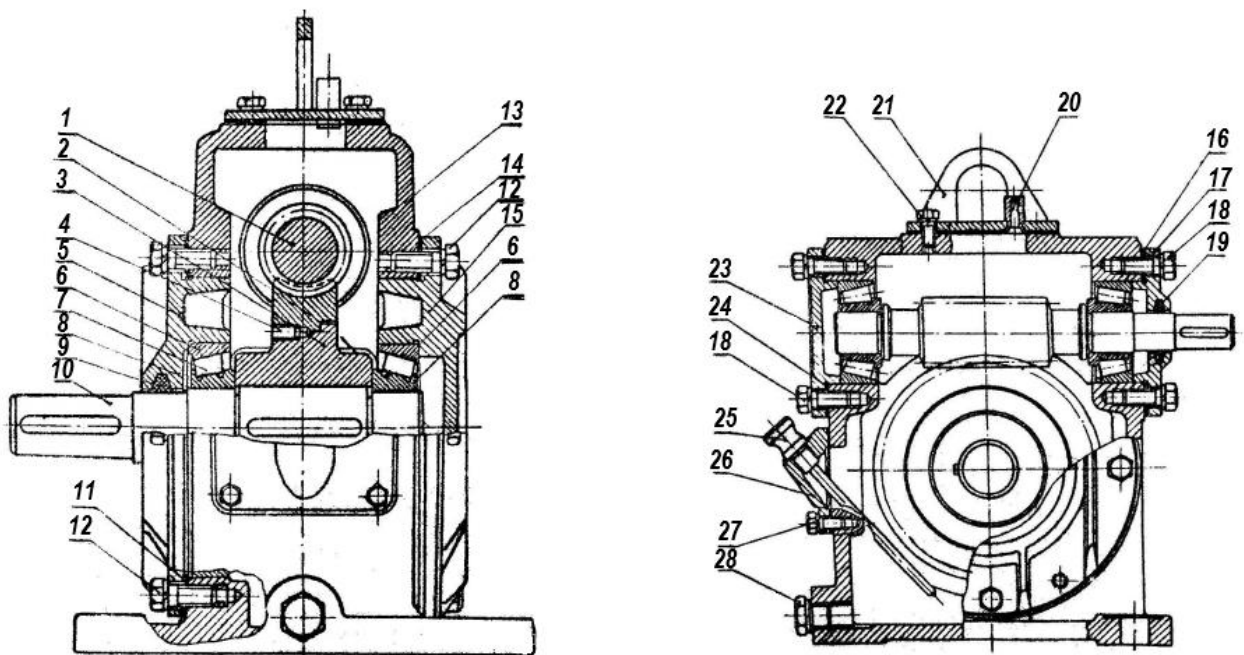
Конструкція одноступічастого черв'ячного редуктора Ч-63
